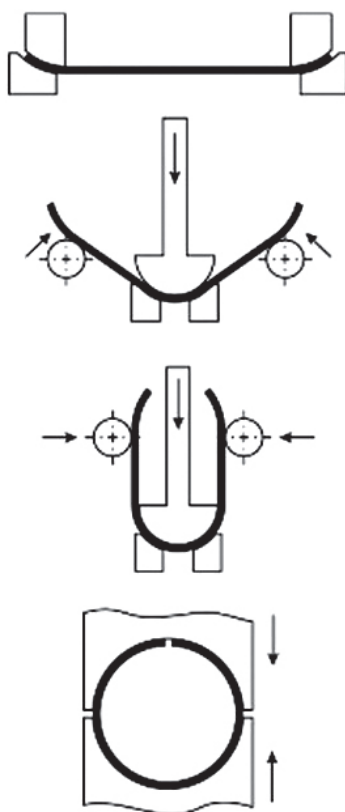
Схема формовки трубной заготовки — UOE-процесс
